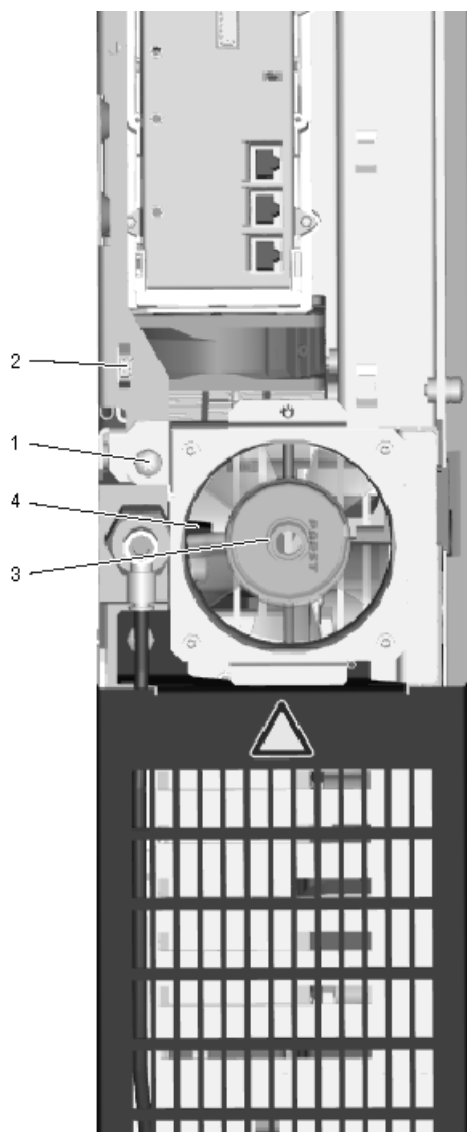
Демонтаж вентилятора электронного оборудования для использования вентиляционного рычага
